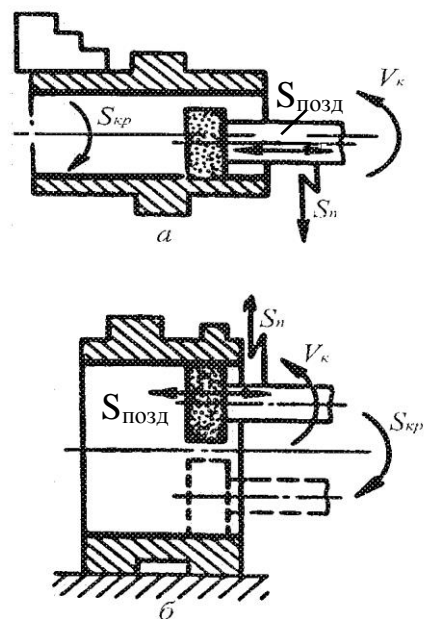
Схеми обробки заготовок на внутрішньо-шліфувальних верстатах
